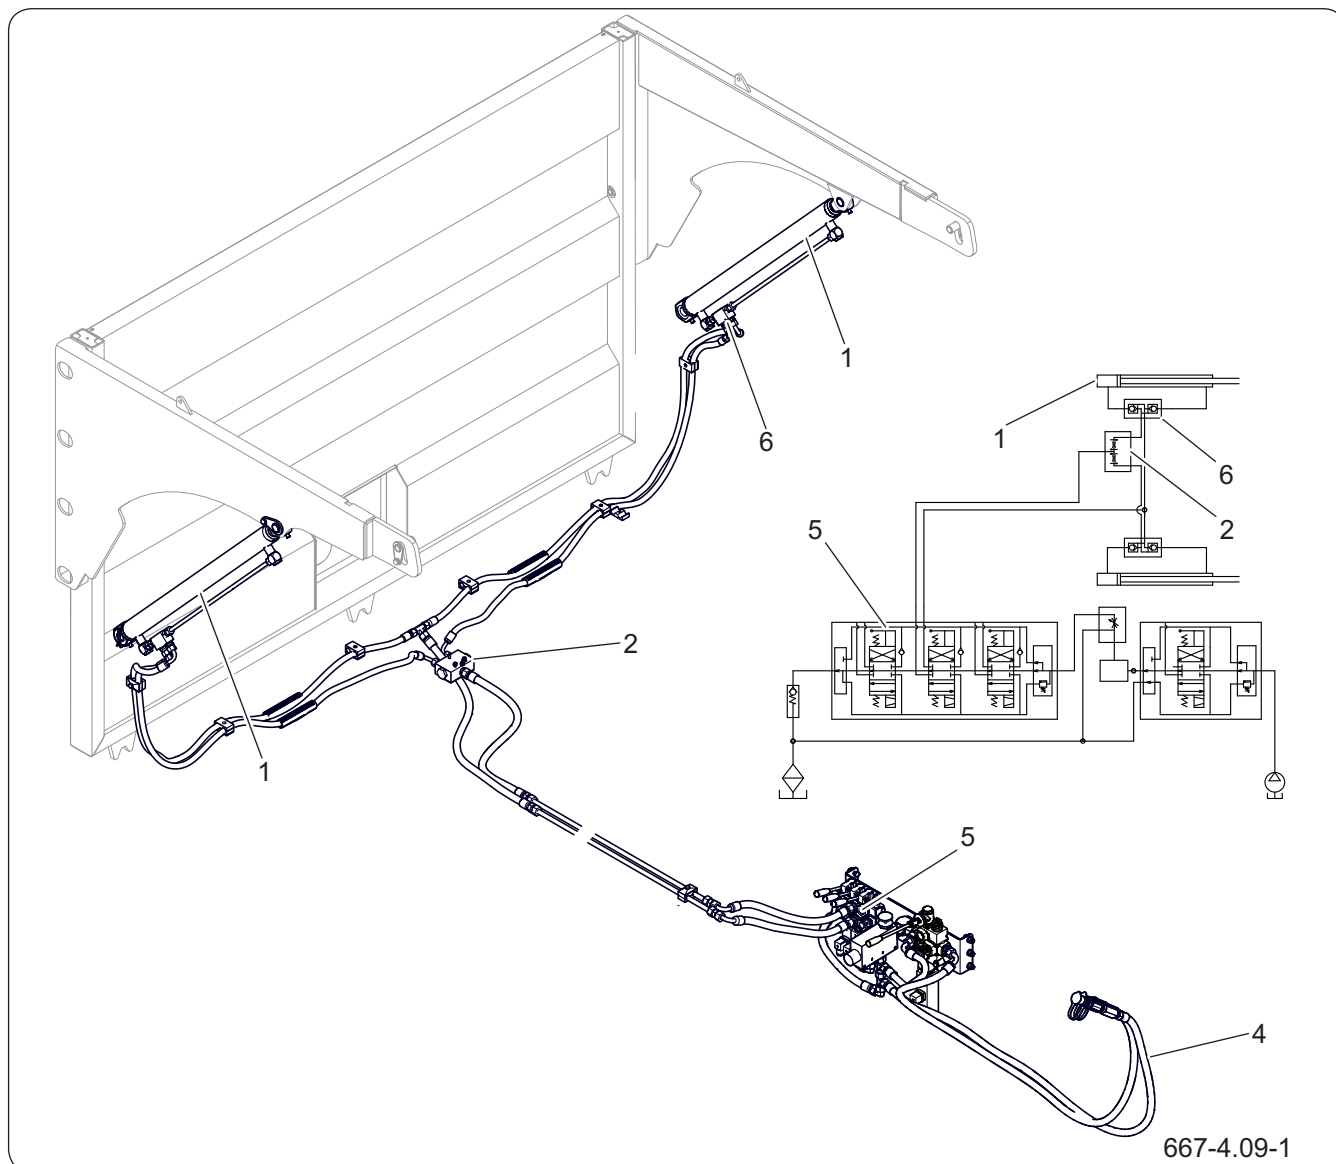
Konstrukce a schéma hydraulické instalace vyklápění pro hydraulické zavěšení
